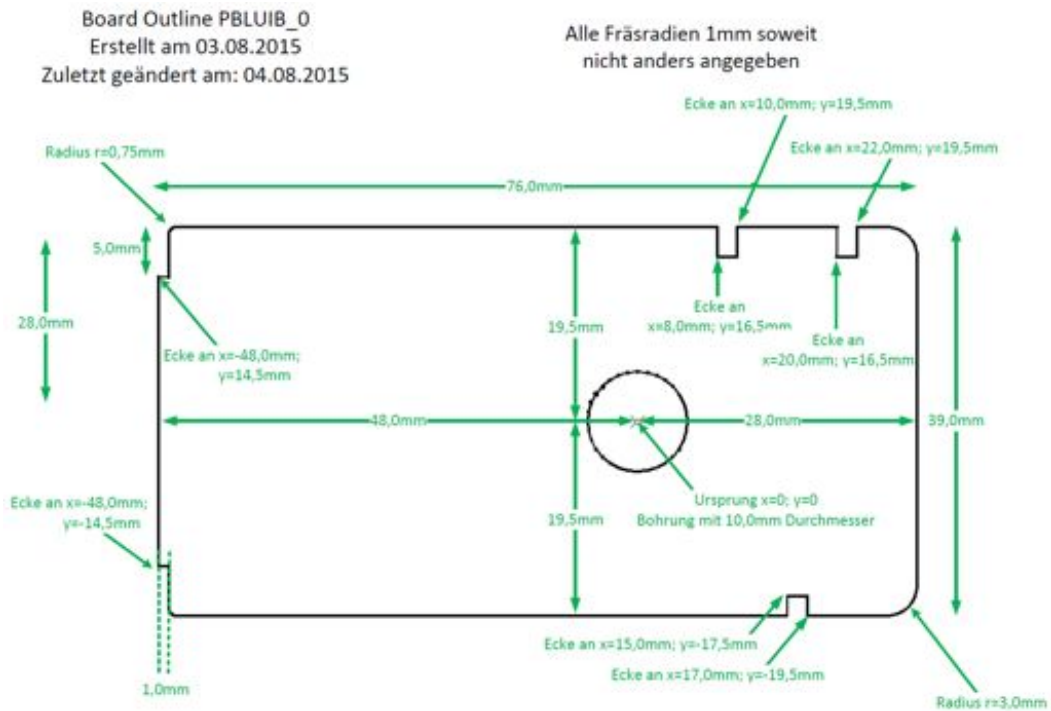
Boardoutline der Baugruppe PBLUIB
